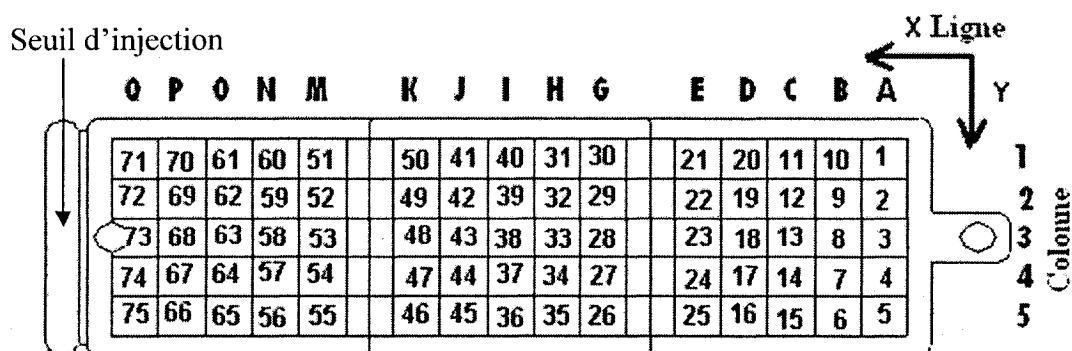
75 points sur la surface d'une éprouvette.
